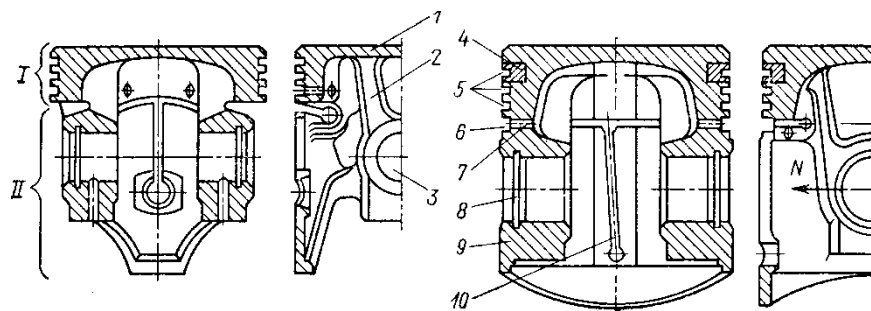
Поршни бензиновых двигателей грузовых автомобилей:
